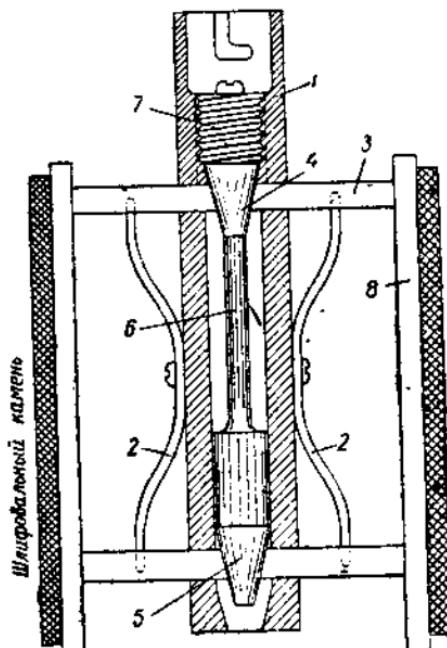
Прибор «Хатто» с шестью камнями для шлифовки цилиндров.
